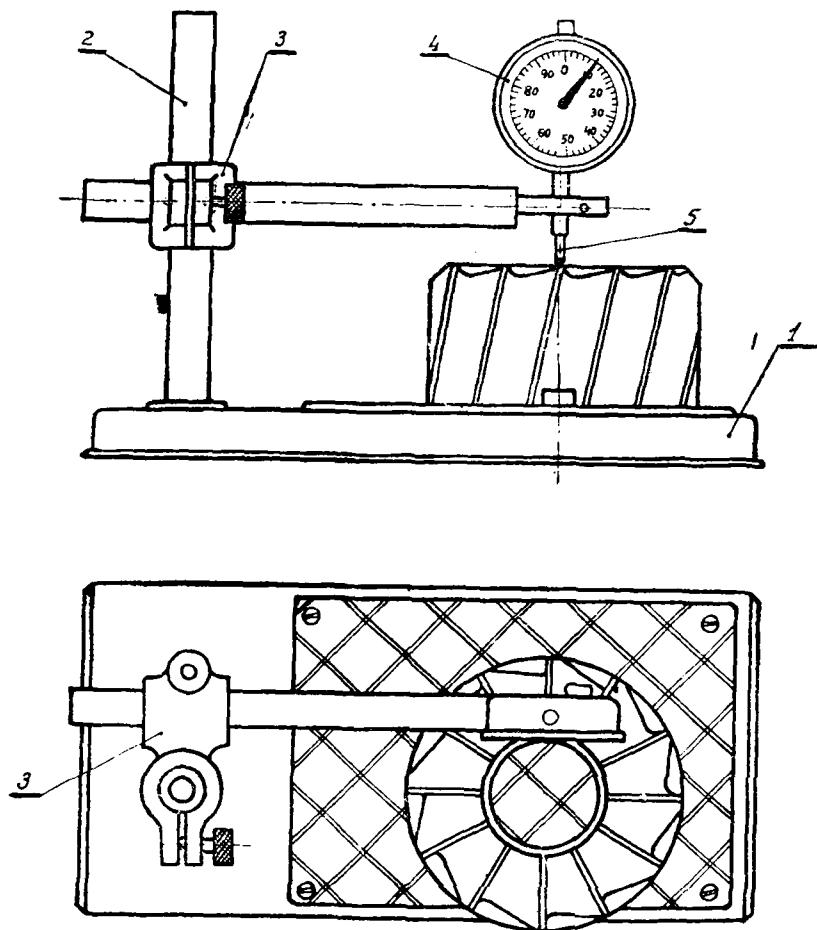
Приспособление для измерения биения торцевых зубьев фрезы
